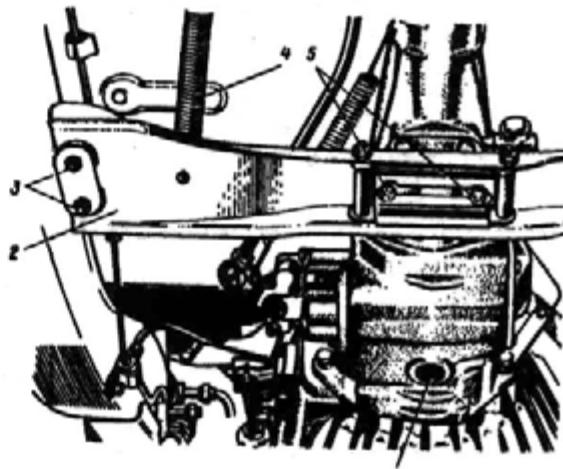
Снятие коробки передач с автомобиля (вид снизу, сзади):
